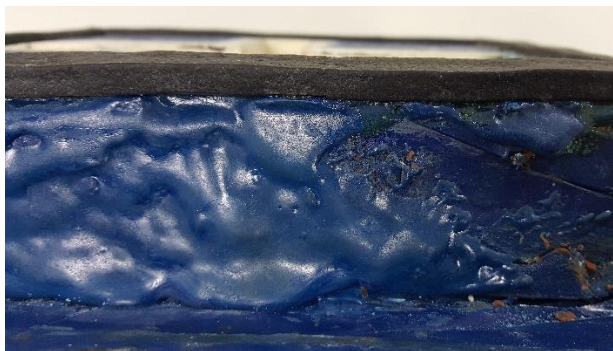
Camada 1 com falha de desmoldagem corrigida
